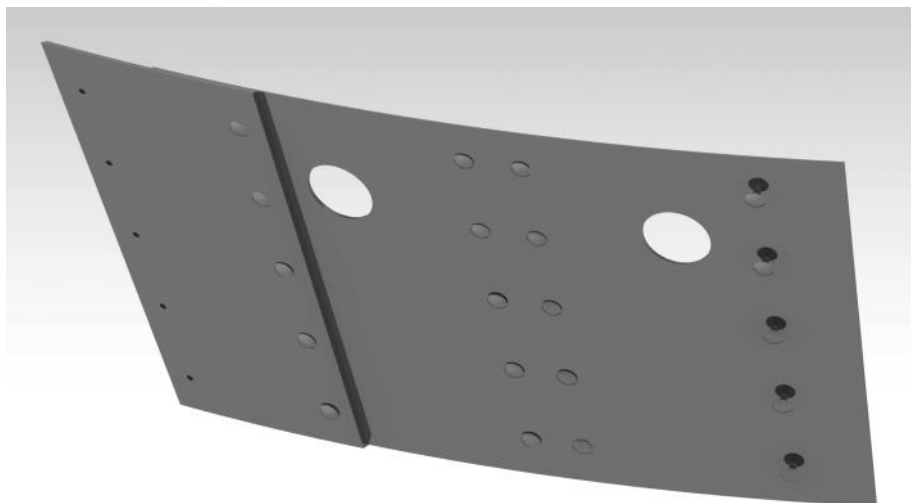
refuerzo y unión entre refuerzos de los tablones de la cubierta inferior
